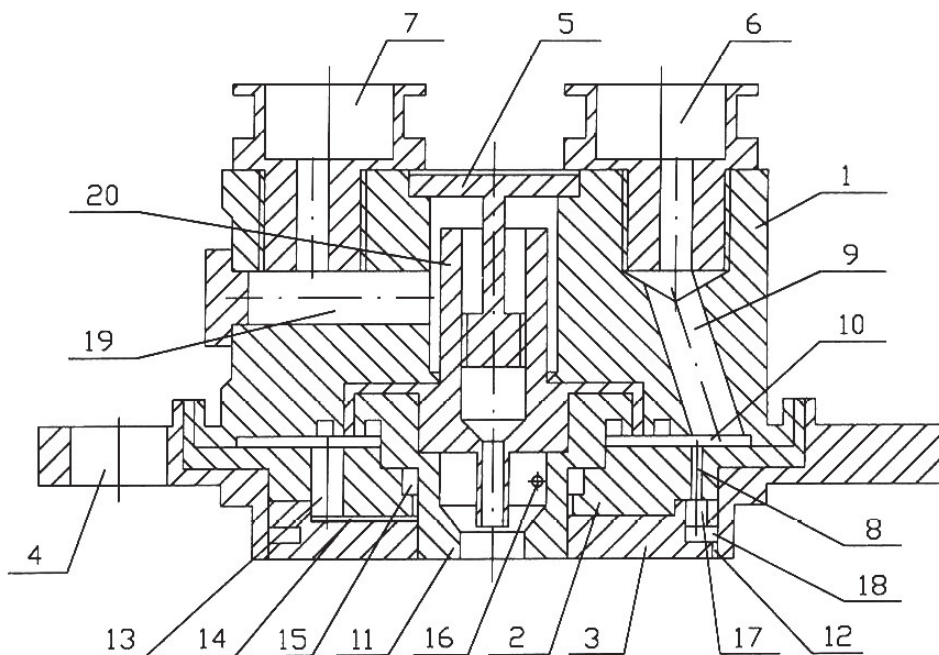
Конструкция однофорсуночной смесительной головки двигателя ДМТ МАИ-200-1: 1 — корпус; 2 — промежуточное днище; 3 — огневое днище; 4 — фланец; 5 — шнек; 6 — вход Г; 7 — вход О; 8, 17 — каналы подвода Г в завесу; 9 — канал подвода Г; 10 — коллектор Г; 11 — форсунка Г; 12 — тангенциальный канал завесы; 13, 14, 15 — каналы подвода Г к форсунке; 16 — подвод Г в форсунку Г; 18 — коллектор завесы; 19 — подвод О; 20 — корпус форсунки О
